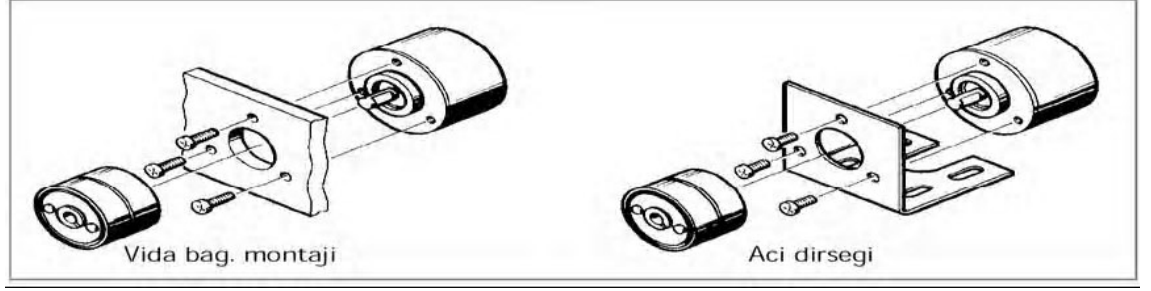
Kare flanşlı şaft enkoderlerin montajı
